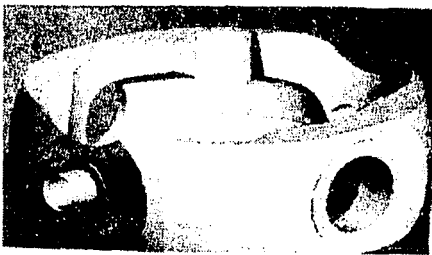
Realización tridimensional de partes de una máquina con sistemas CAD
